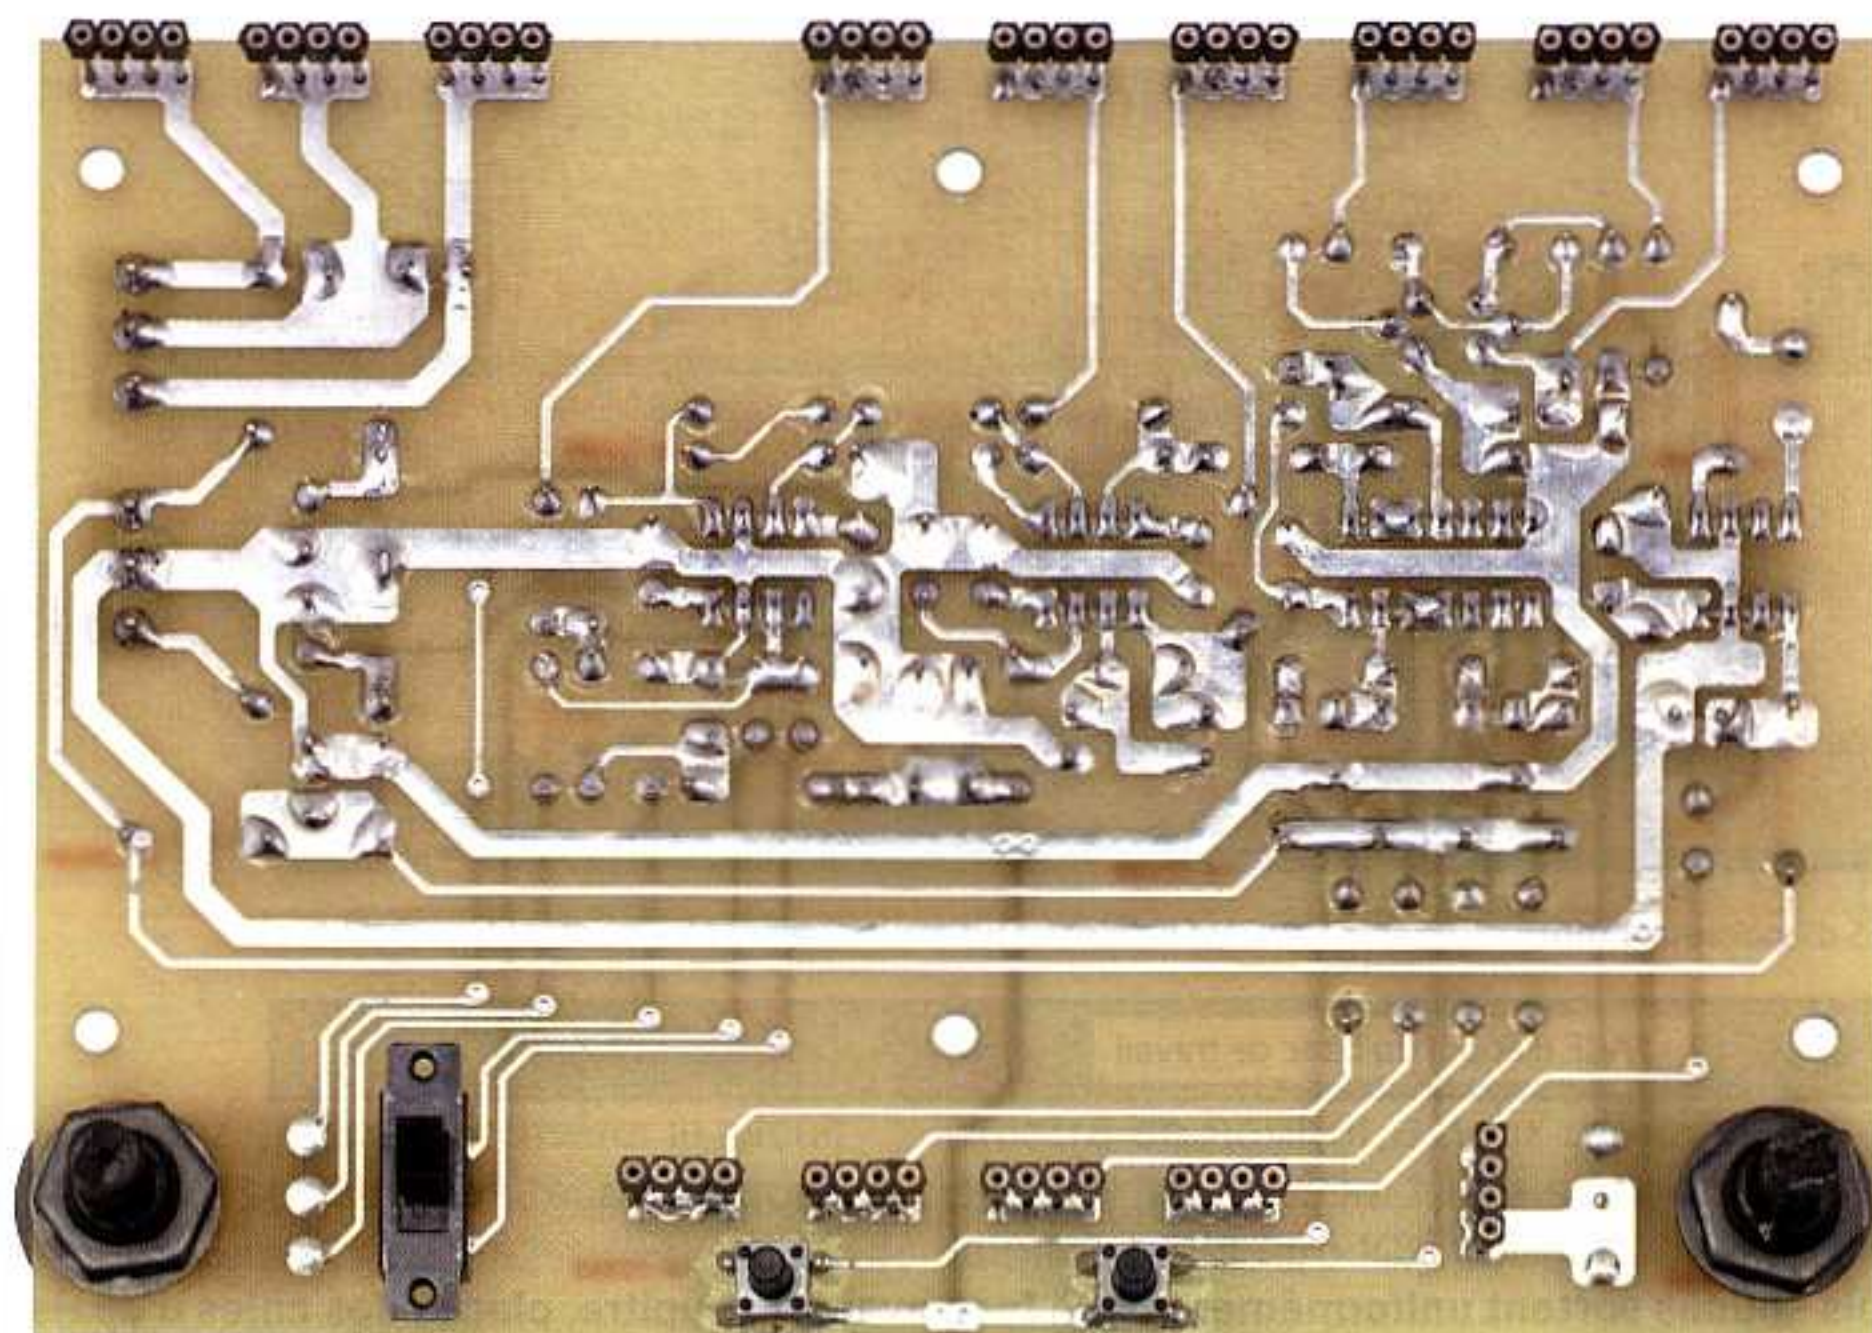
Photo d'un des prototypes de la platine de base EN3001 du MINILAB EN3000, côté soudures.
